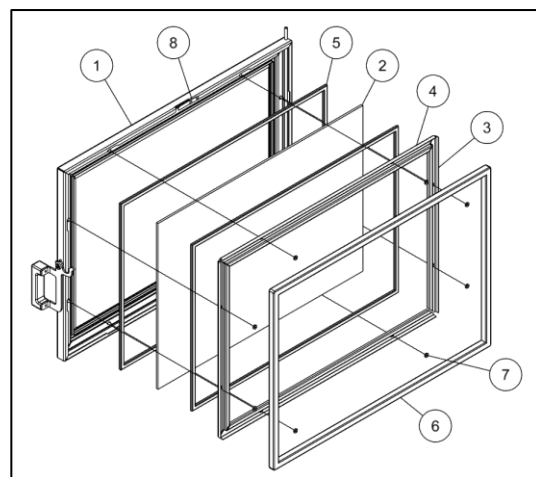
Vue éclatée de l'assemblage de la porte
